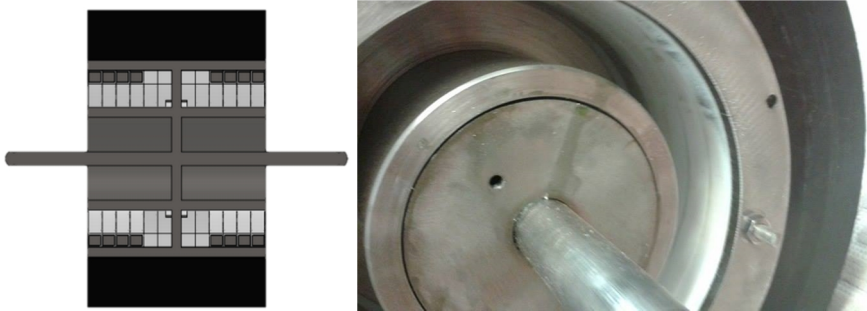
Assemblaggio gruppo magneti nel rotore
